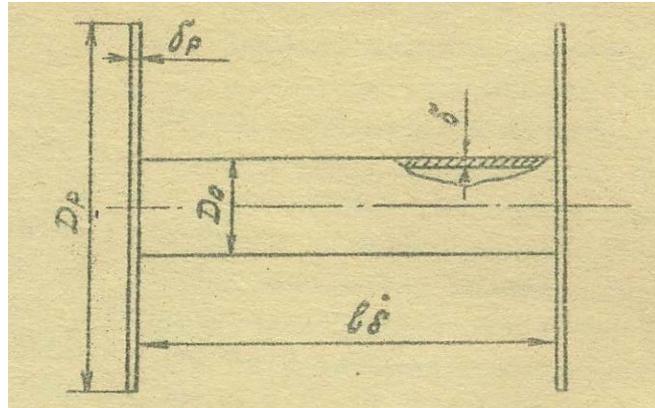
Теоретический чертеж навивного неводовыборочного барабана
